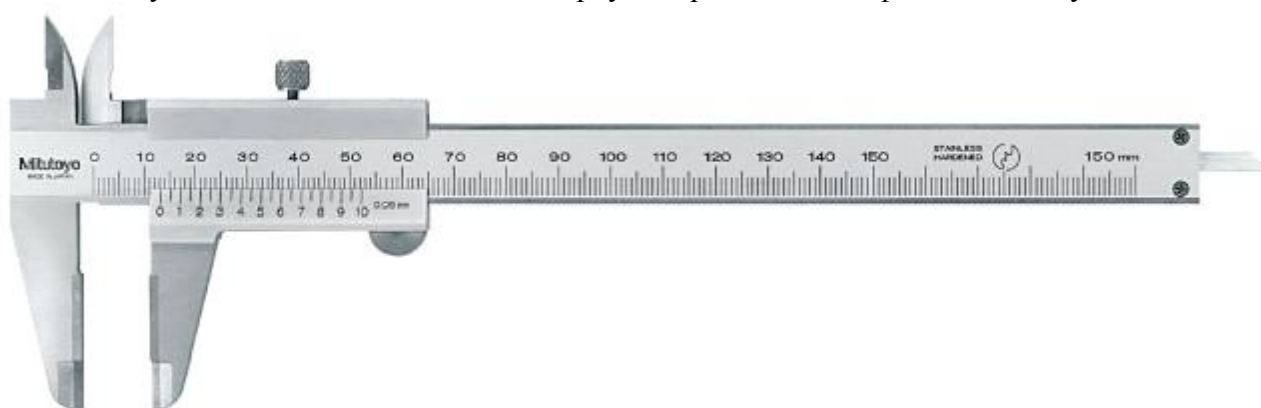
Общий вид штангенциркуля серии 530 модификации нониусные с твердосплавными измерительными губками
